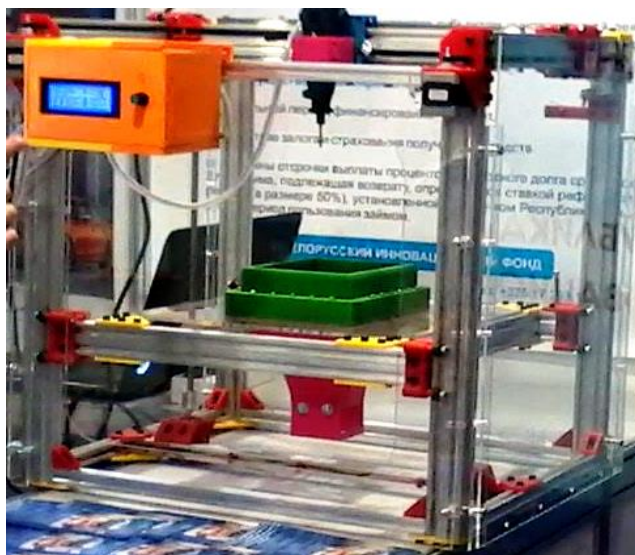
МФУ с установленными модулями для 3D фрезерования и фотополимерной печати
